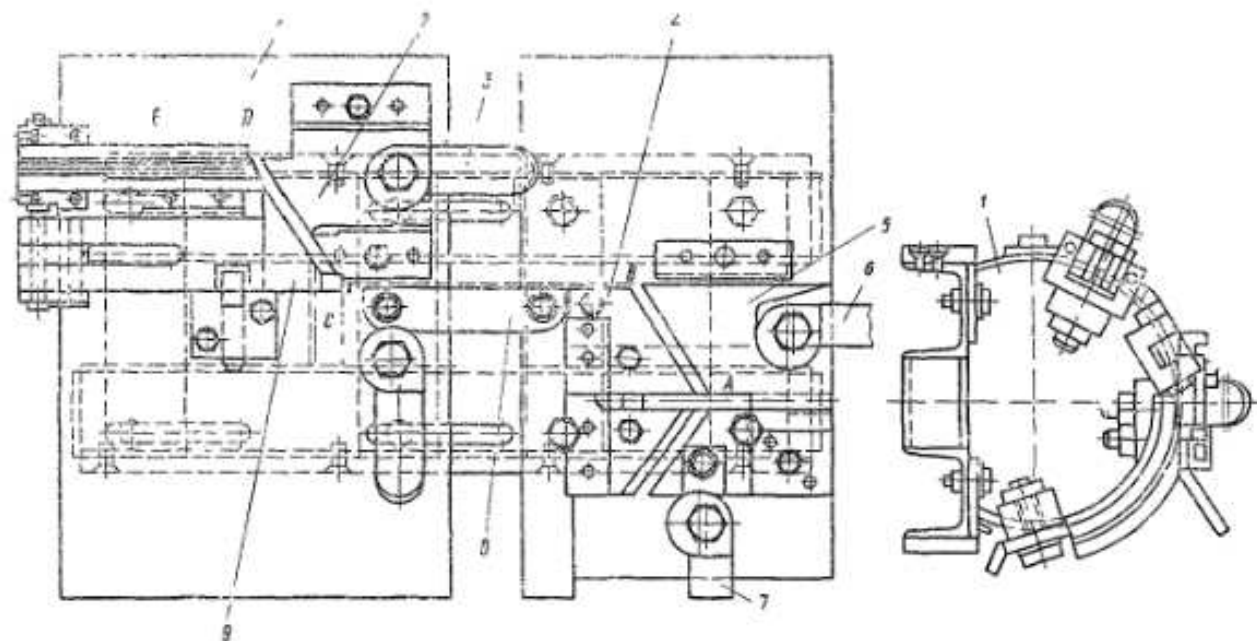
гибочное приспособление для выгибания и формовки лобовых частей волновой стержневой обмотки якоря
